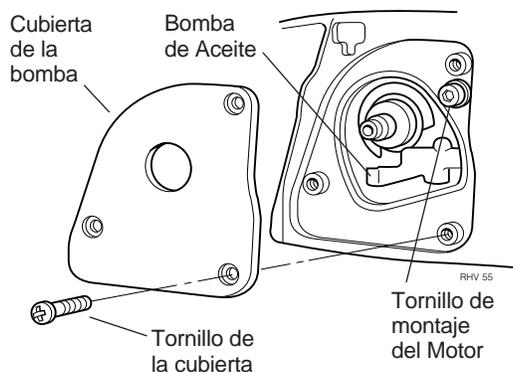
Cubierta de la Bomba y Montaje de Motor
